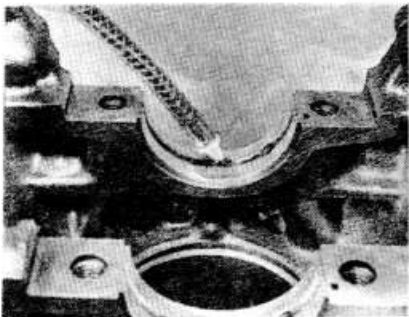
Смажьте вкладыш коренных подшипников перед установкой коленвала
